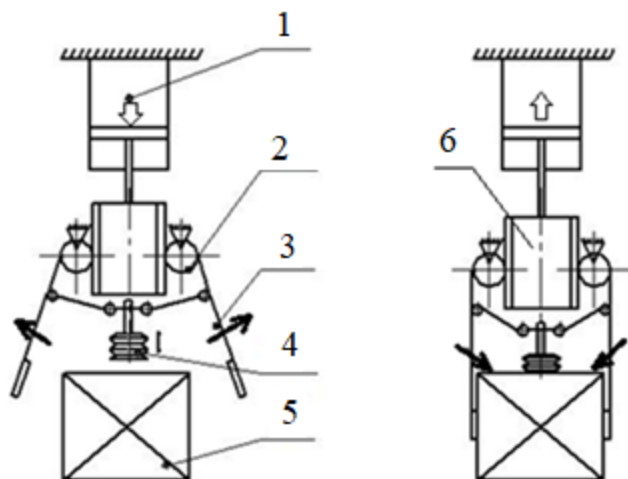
Схема комбінованого захоплювального пристрою механічно-вакуумного типу з коливальним рухом стулок: 1- пневмоциліндр; 2- циліндричні колеса; 3- стулки; 4 – вакуумний елемент; 5 – упаковка; 6 – зубчата рейка; а- початкове положення пристрою; б - пристрій в момент захоплення упаковки
